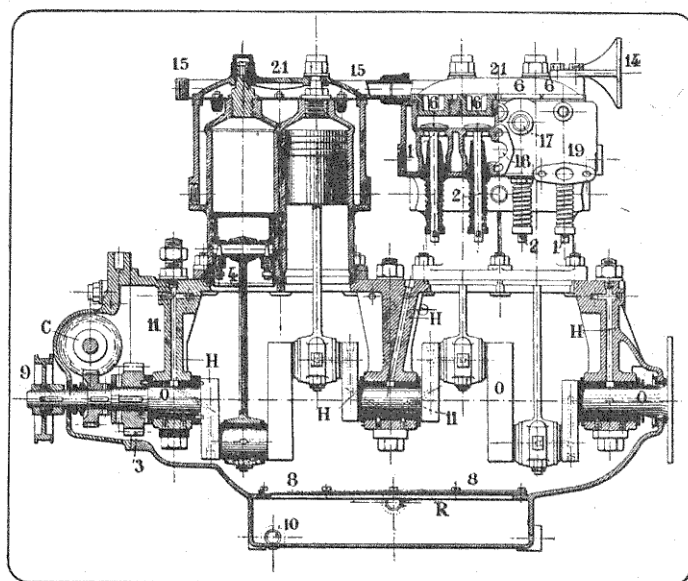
Coupe du moteur de la fig. 73. — 0, arbre vilebrequin. — 2, clapets d'aspiration. — 3, engrenage de distribution du moteur. — 6, bouchons des clapets. — 8, tamis d'huile. — R, réservoir d'huile.
